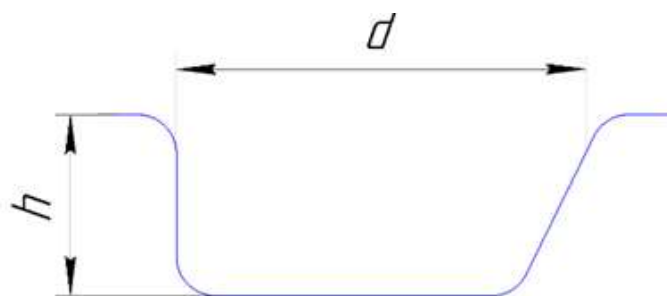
Форма и размеры ячейки цилиндрического триера
